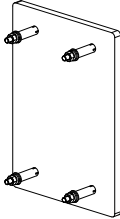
Dehnschrauben in die Löcher bohren
